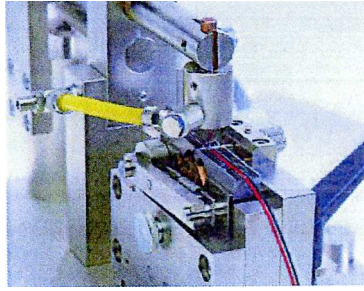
6. El termopar es soldado a la muestra mediante “spot welding”
